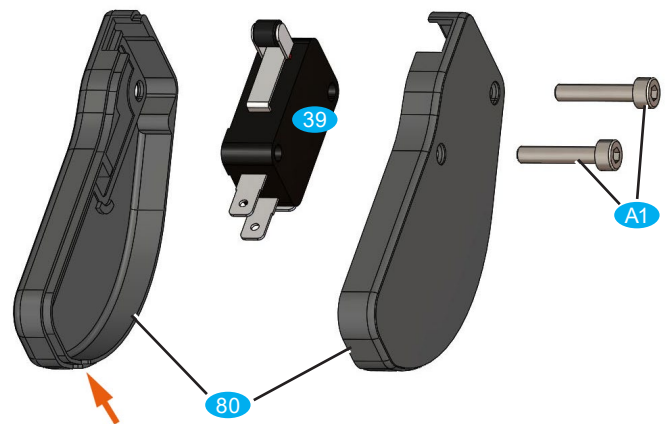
Baugruppe Referenzschalter / Gehäuse.
